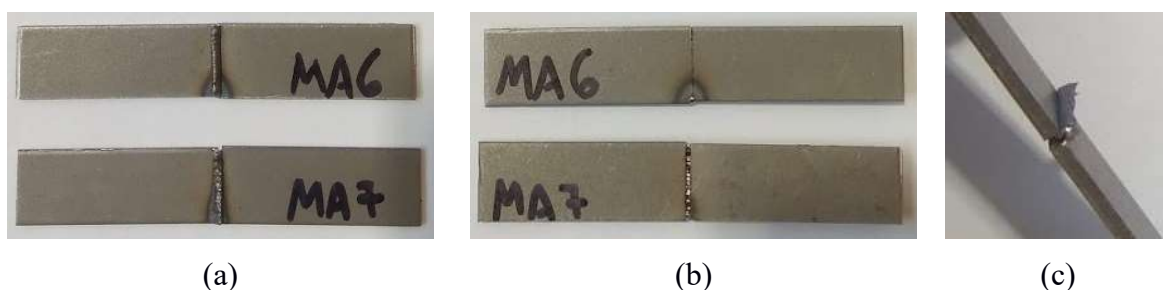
Amostras MA6 e MA7. (a) parte superior. (b) raiz da soldadura. (c) detalhe do metal de adição não depositado na junta
